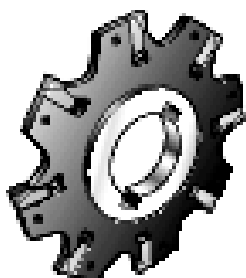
Конструкция прорезной фрезы Шведской фирмы Sandvik Coromant с механическим креплением специальных режущих пластин
